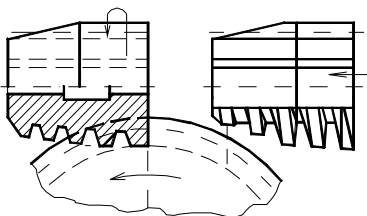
Способ нарезания червячного колеса с тангенциальной подачей [65]
